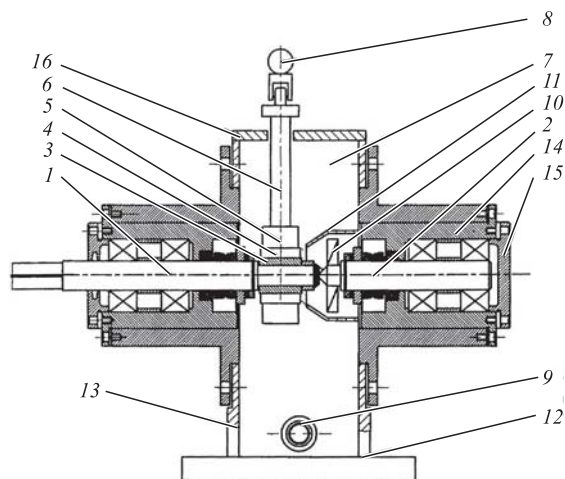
Стенд для испытаний образцов на износостойкость: 1, 2 — вал; 3 — внутренняя втулка; 4 — внешняя втулка; 5 — обойма; 6 — шток; 7 — корпус; 8 — рычаг; 9 — штуцер; 10 — лопастное колесо; 11 — кожух; 12 — стенка корпуса; 13 — вторая стенка корпуса; 14 — цилиндрический корпус; 15, 16 — крышки
